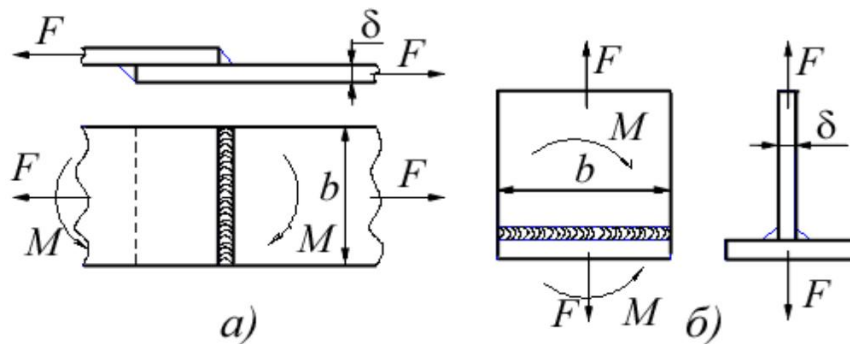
Схемы нагружения сварных соединений выполненных угловым швом:
